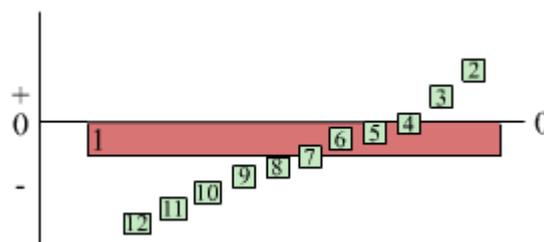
Взаємне розташування полів допусків сполучуваних деталей у системі вала: 1 — поле допуску основної деталі системи;
